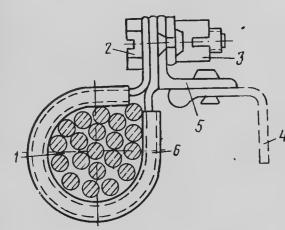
Крепление электрожгута при помощи переходного уголка: 1—электрожгут; 2—болт; 3—анкерная гайка; 4—деталь конструкции; 5—переходный уголок; 6—хомут
